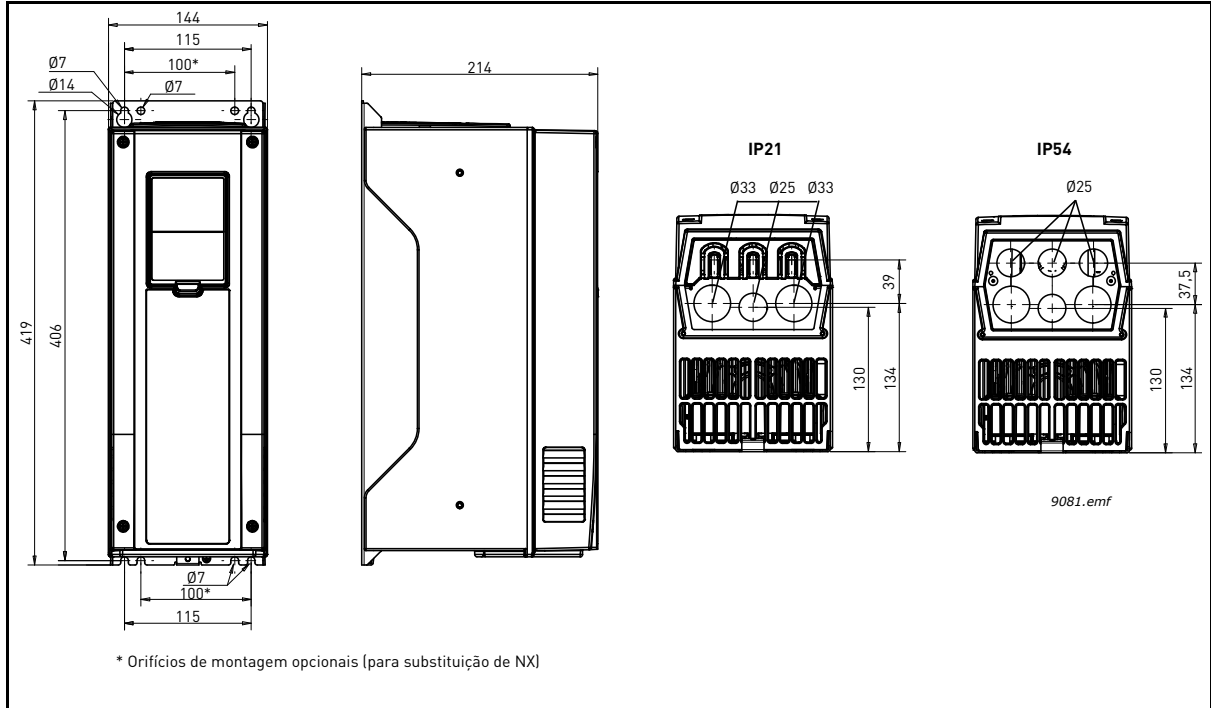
Dimensões do inversor de CA Vacon, MR5, montagem na parede
